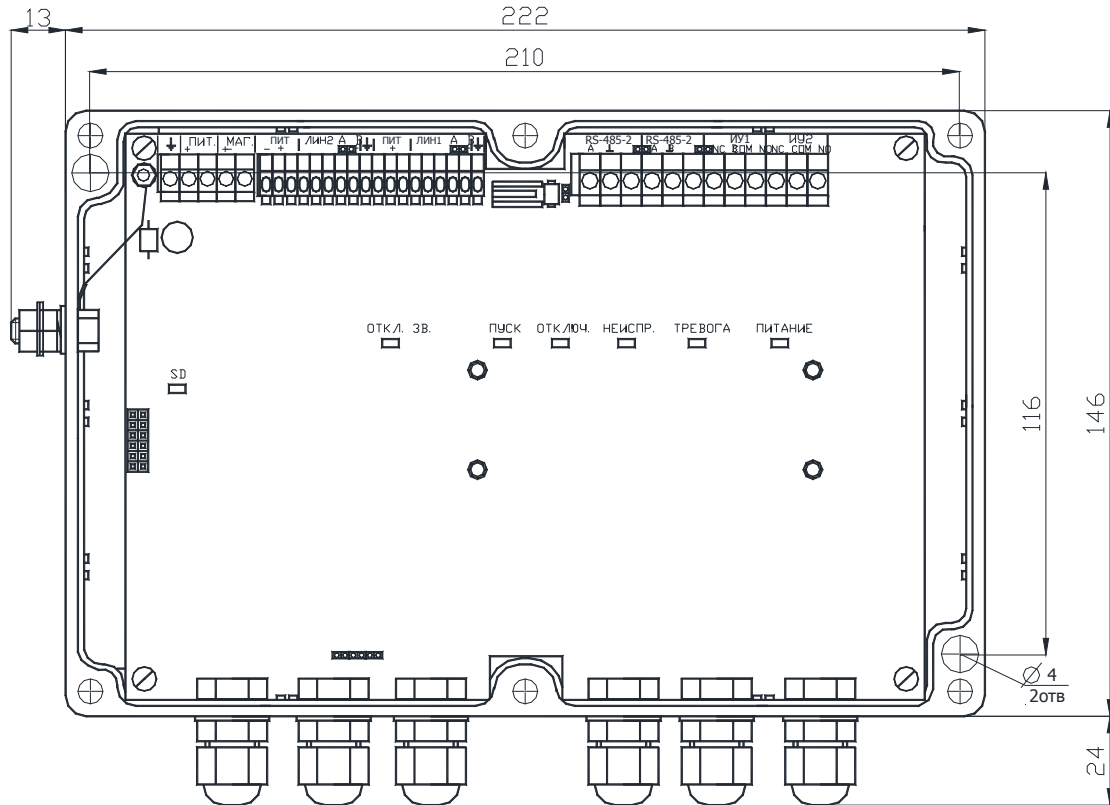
Общий вид линейного блока со снятой крышкой
